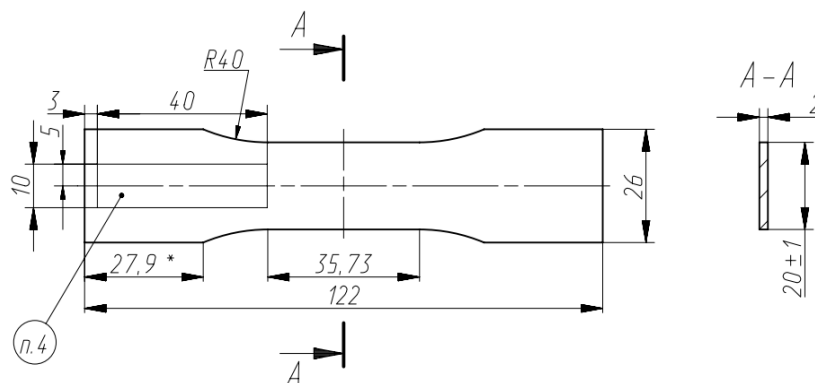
Схематичный вид заготовки для усталостных лабораторных испытаний
